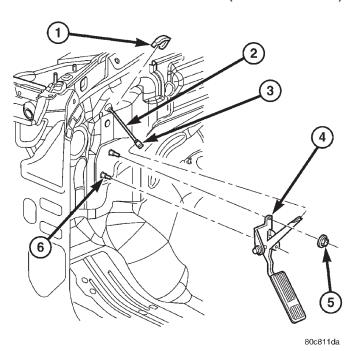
CONJUNTO DE PEDAL DEL ACELERADOR Y SOPORTE
